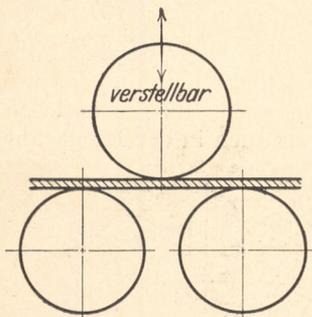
Schema der Dreiwalzen-Biegemaschine.
